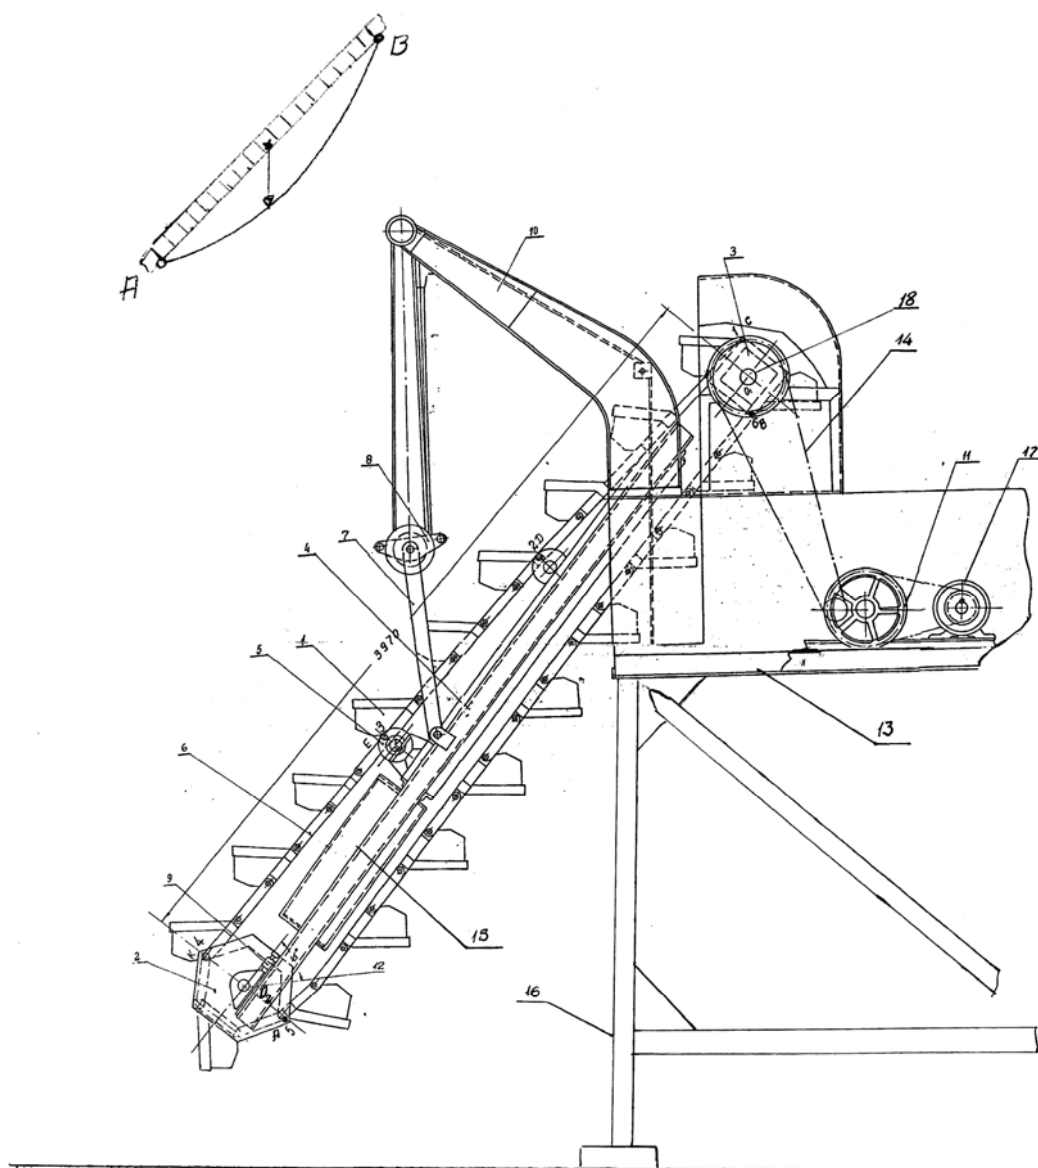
Испытательный стенд с цепным рабочим органом УПМ-1.
